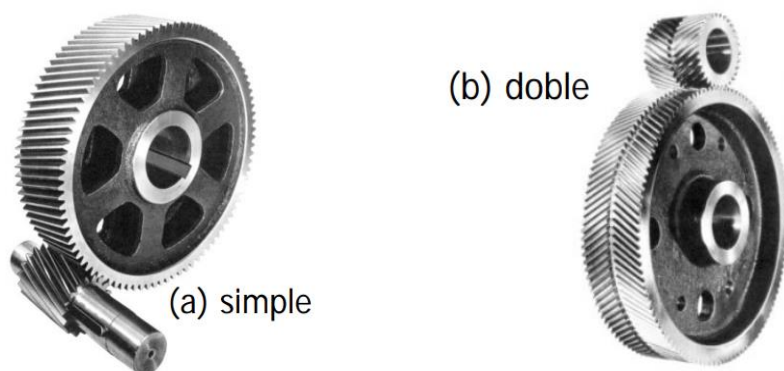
(a) Engranaje cilíndrico de dientes helicoidales simple. (b) Engranaje cilíndrico de dientes helicoidales doble^{xx}.
